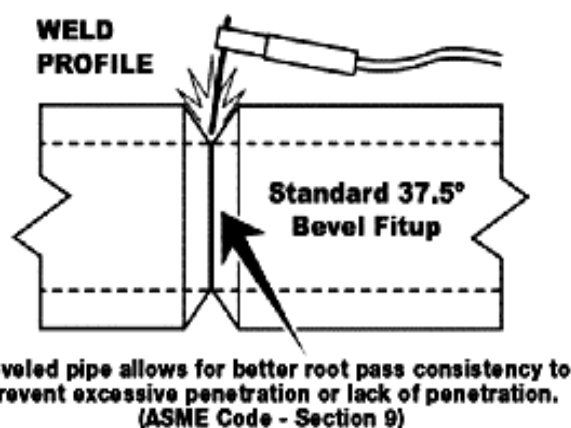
Verbesserung der Qualität des Schweißens
